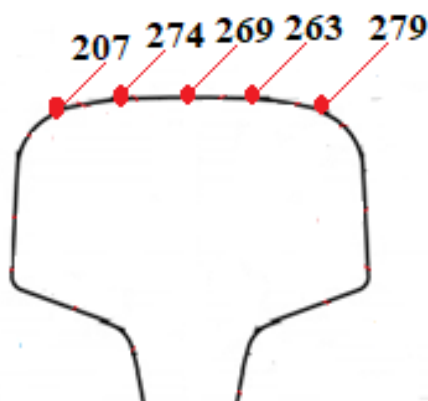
Измерение твердости металла на поверхности катания нового рельса ENSIDESA 01 16 60 E1
